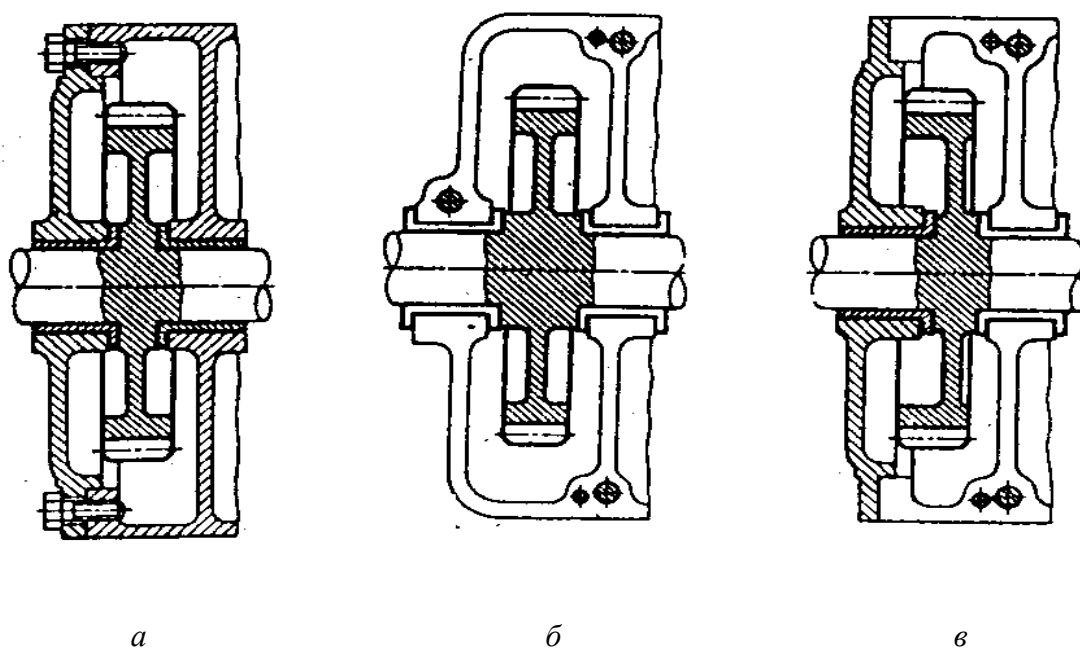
Виды сборки составных частей шестеренчатого вала в корпусе: *а* - аксиальная сборка; *б* - радиальная сборка; *в* - смешанная (радиально-аксиальная) сборка
